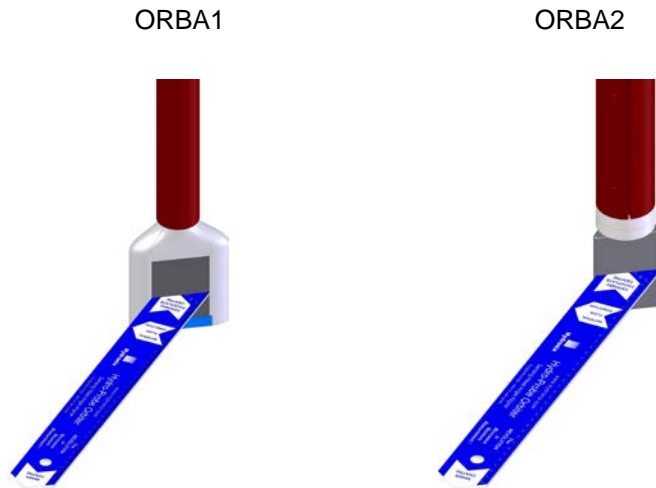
Приспособление для установки угла лицевой пластины датчика Hydronix
